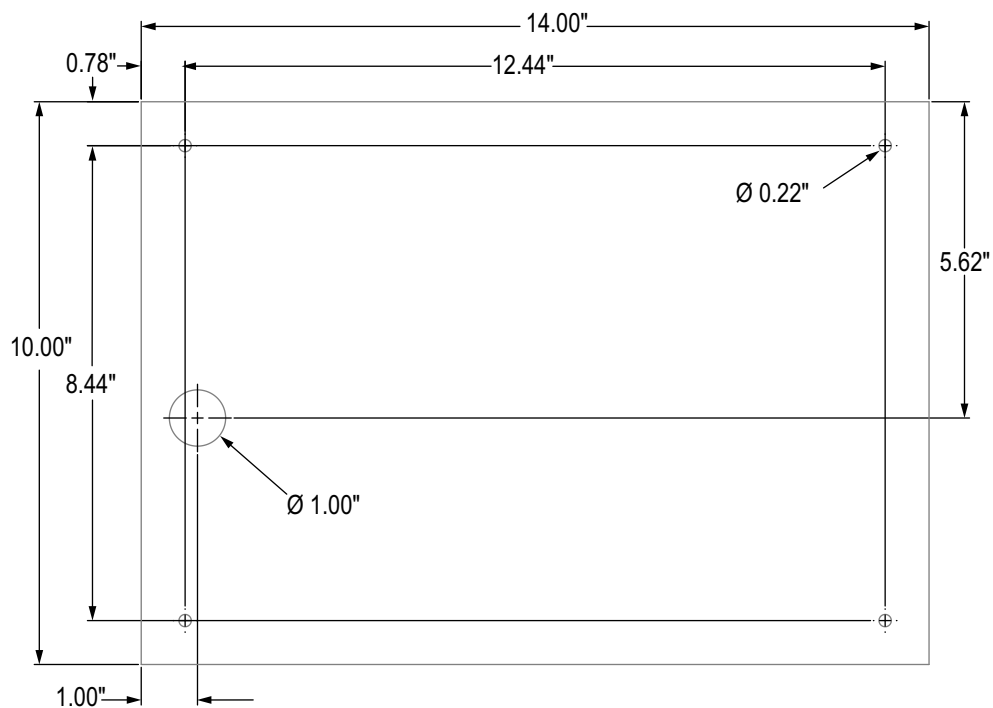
Dimensiones para el montaje en panel únicamente del visor táctil de 12"
